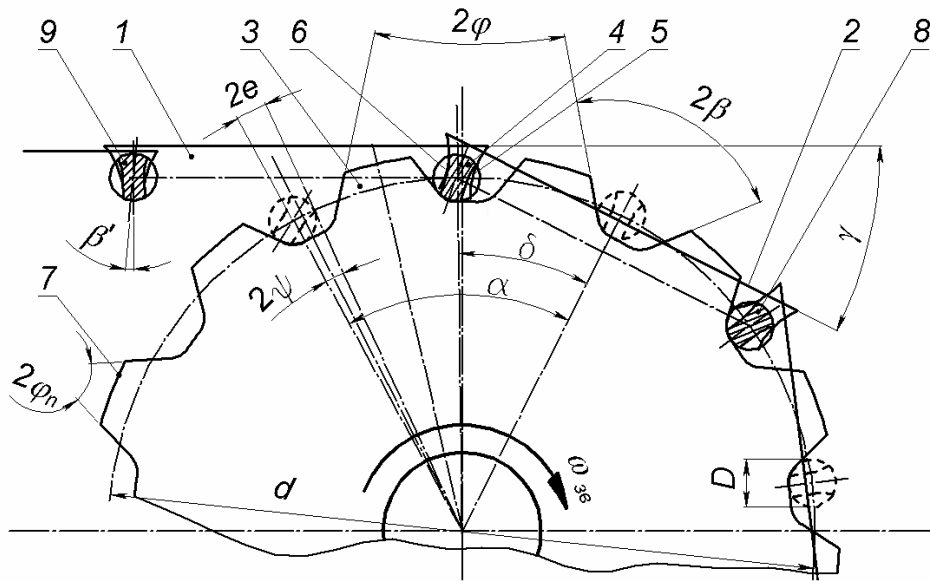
Схема розташування ланцюга з шарнірами тертя кочення на двоходовій зірочці: 1 і 2 – ланки ланцюга; 4, 9 і 8 – валики ланцюга; 3 і 7 – зуби зірочки; 6 – опукла робоча поверхня отвору пластини; 5 – увігнута робоча поверхня валика
